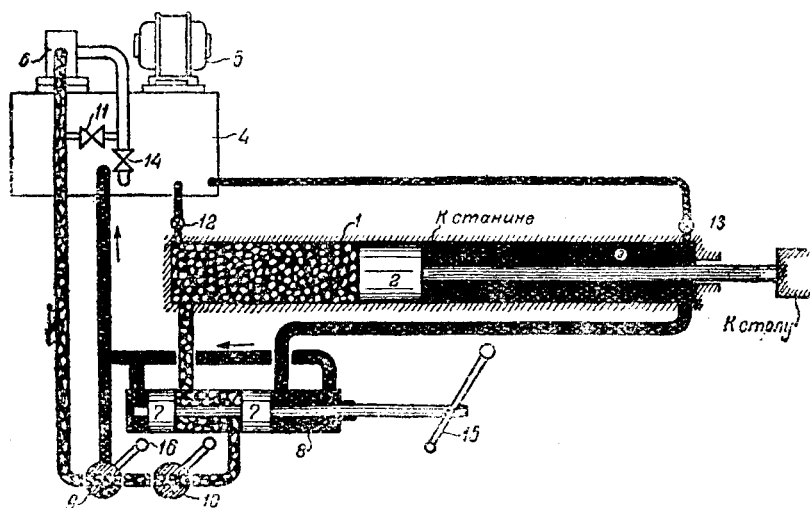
Схема гидравлической подачи стола станка „Шмальц“
